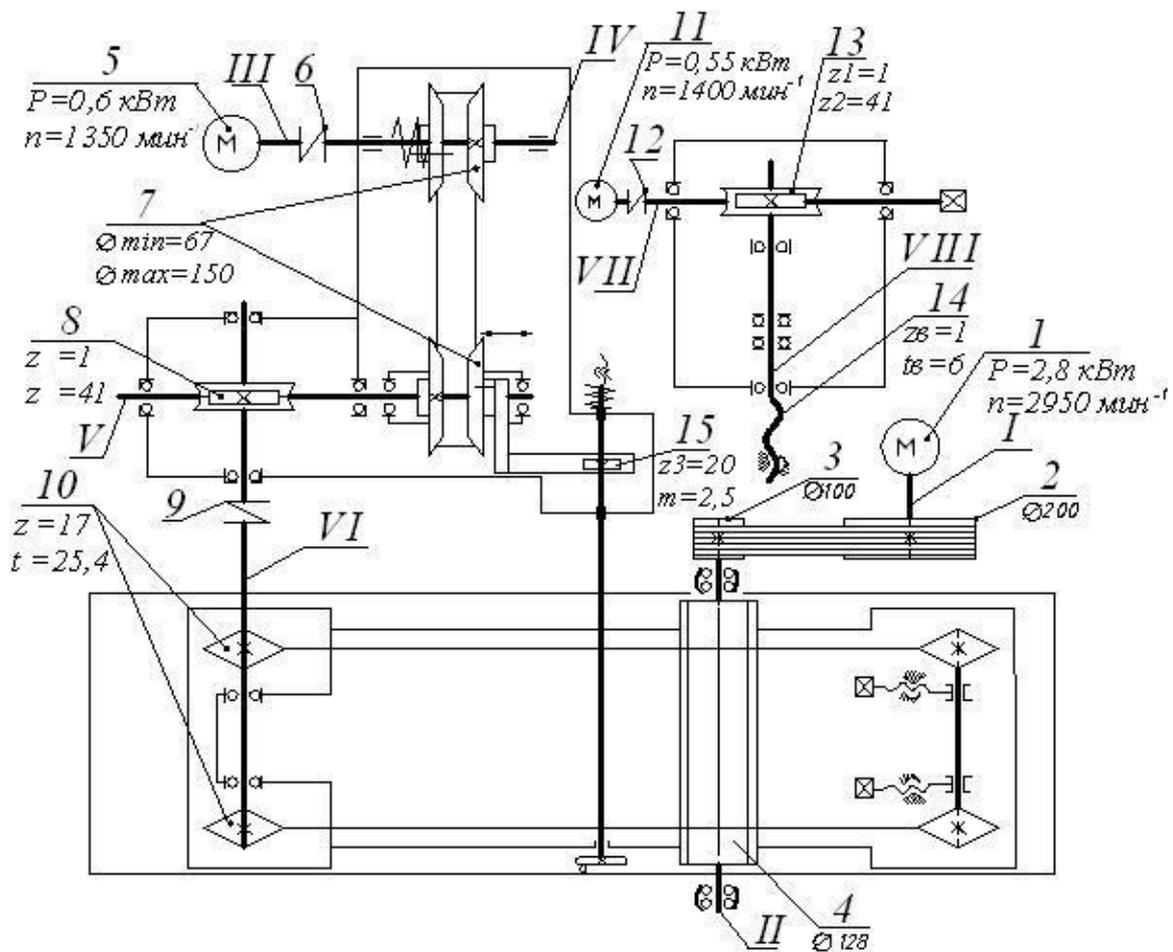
Кинематическая схема фуговального станка с конвейерной подачей СФК4
